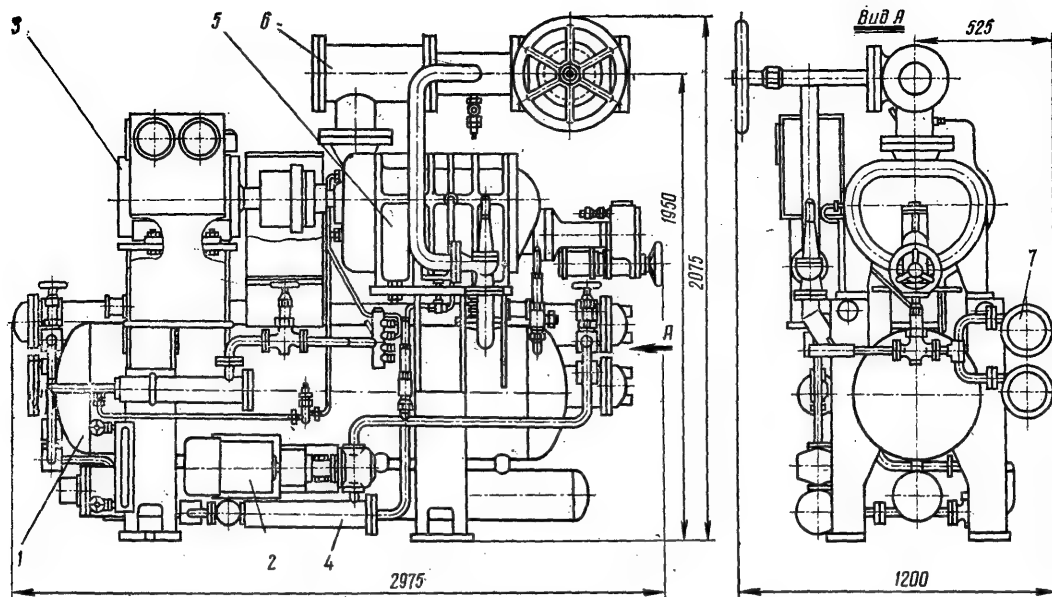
Винтовой поджимающий компрессорный агрегат АН130-7-6:
